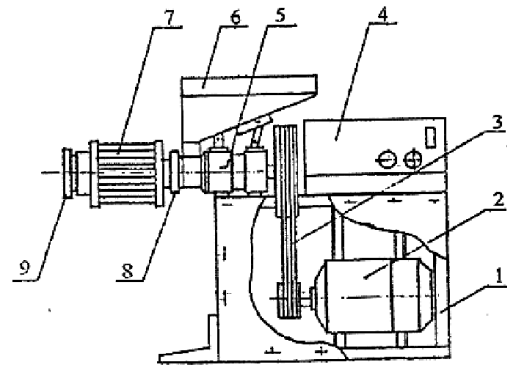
Кинематическая схема маслопресса-ММП-150/50
